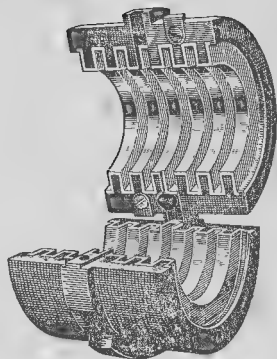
Вкладыш гребенчатого упорного подшипника
